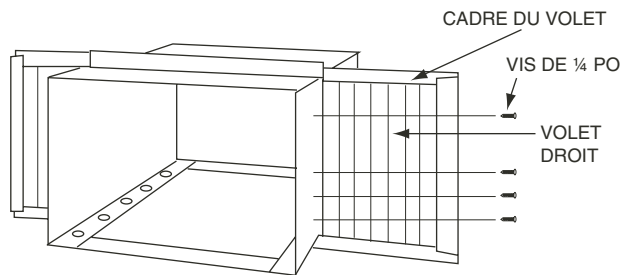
INSTALLATION DES VOILETS LATÉRAUX
